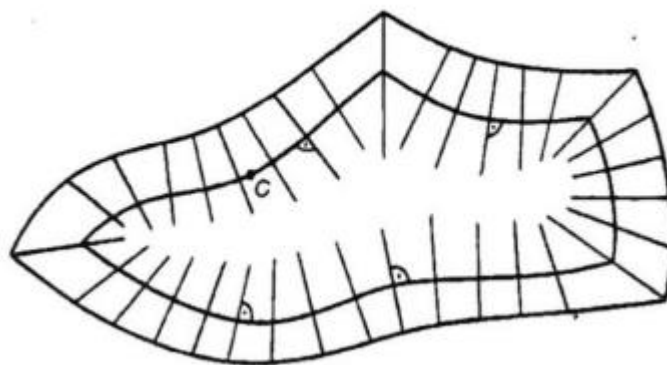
Підготовка шаблонів і одержання розгортки з бокових поверхонь.
